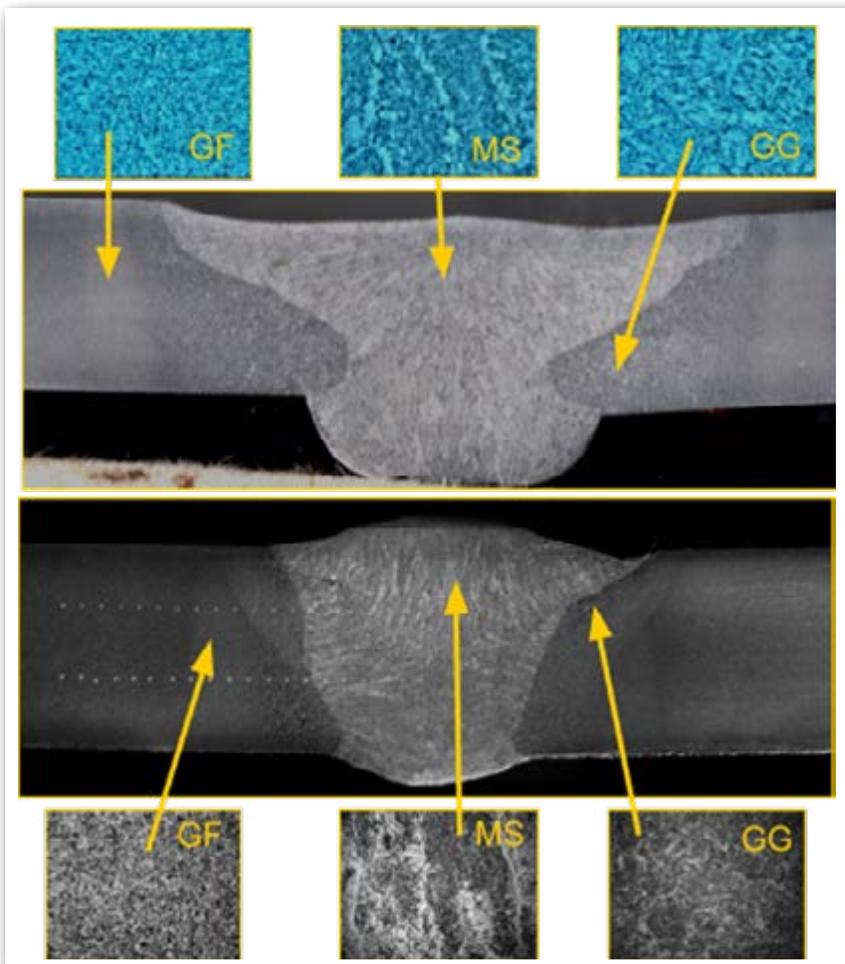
Junta a tope soldada. a) Proceso FCAW, b) Proceso GMAW
